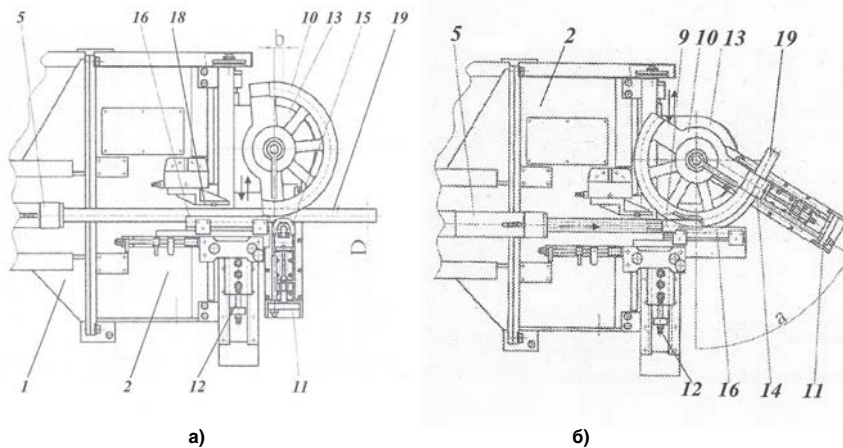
Работа гибочной головки станка в режиме обкатки трубной заготовки вокруг гибочного шаблона и намотки трубной заготовки на гибочный шаблон: а) обкатка трубы, исходное положение; б) намотка трубы, конечное положение
